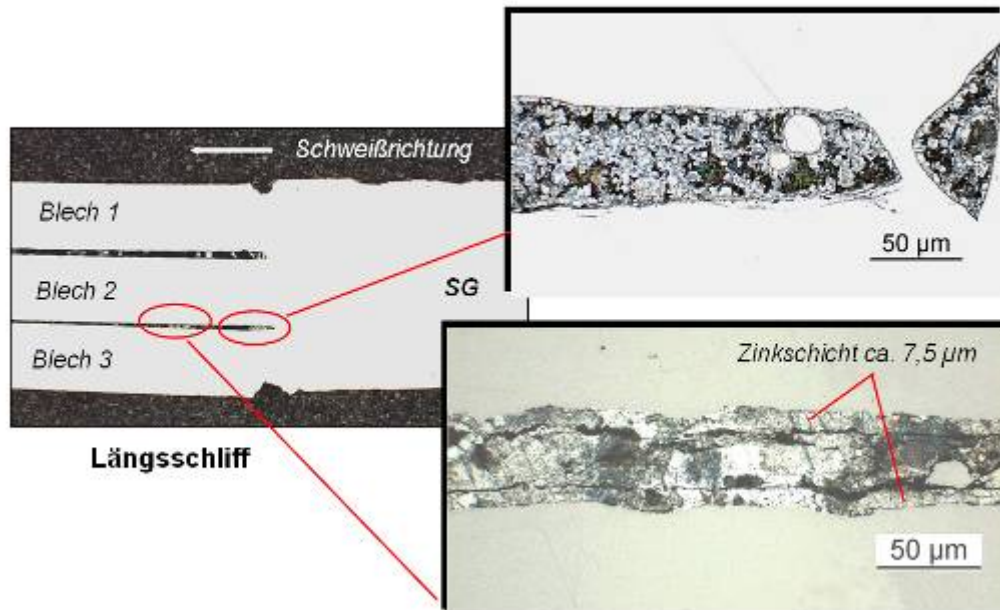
Längsschliff eines laserstrahlgeschweißten Dreifachüberlappstoßes mit Zinkansammlung vor dem Schweißbad; geschweißt mit technischem 0-Spalt; Werkstoff DC04+ZE
